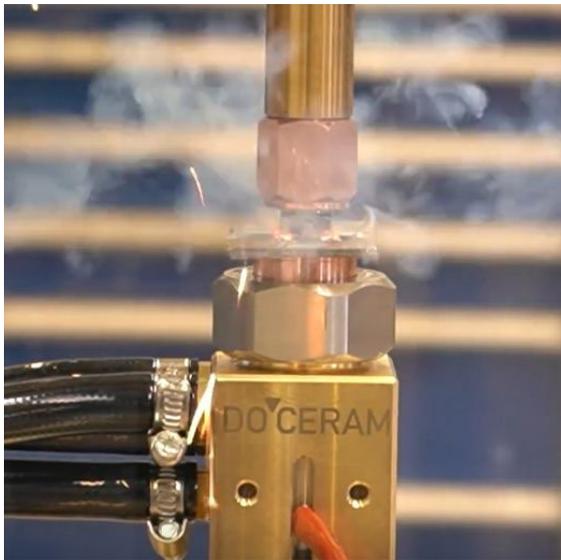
Buckelschweißen Mutter M8-DIN928
